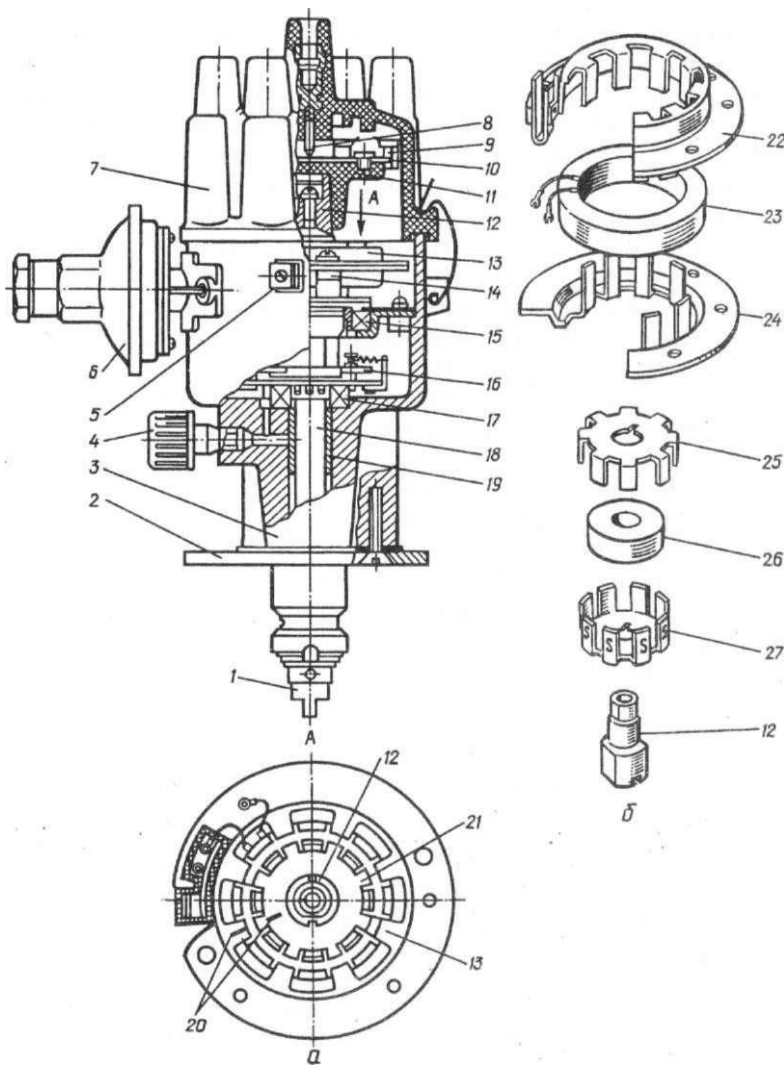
Датчик-розподільник 24.3 706: а - загальний вигляд; б - конструкція датчика; 1 - приєднувальний шип; 2 - пластина; 3 - корпус; 4 - маслянка; 5 - вивід; 6 - вакуумний регулятор; 7 - кришка; 8 - вугільний контакт; 9,10- електроди; 11 - бігунець-розподільник; 12 - втулка; 13 - статор; 14 - опора; 15,17, 19 - підшипники; 16- відцентровий регулятор; 18 - вал; 20 - позначки, 21 - ротор; 22, 24 - полюсні пластини; 23 - обмотка; 25, 27 – обойми
